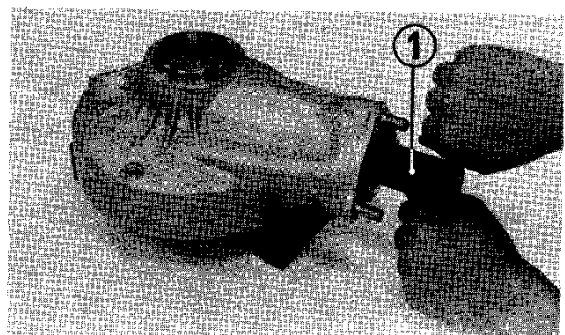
(1) Wellenringdichtung-Ausbauwerkzeug B
